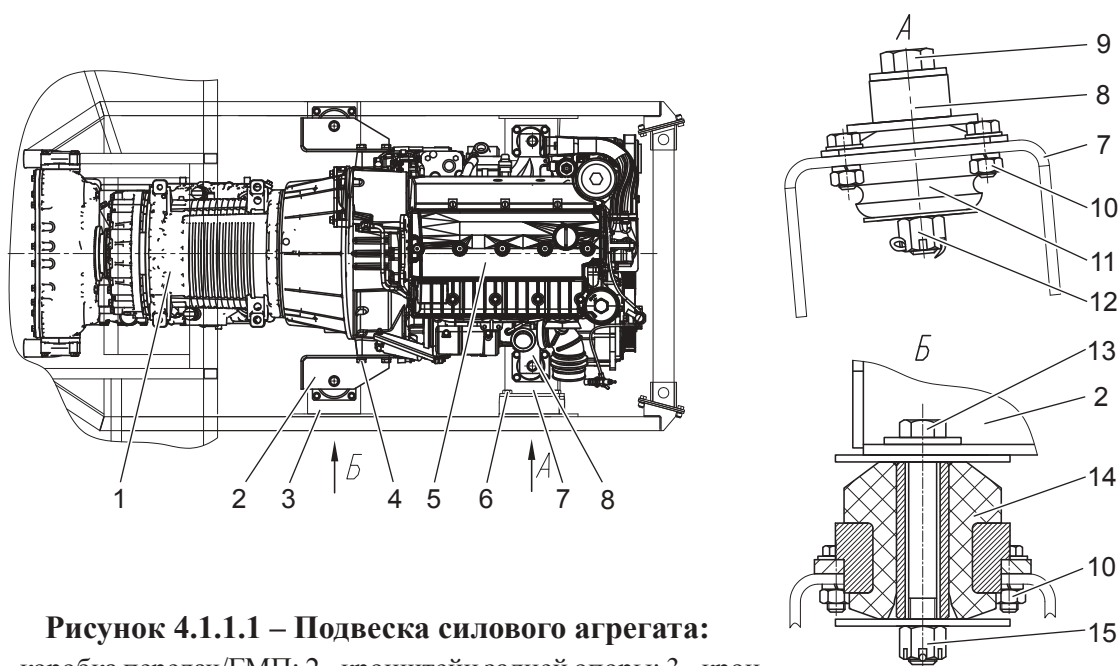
Подвеска силового агрегата:
